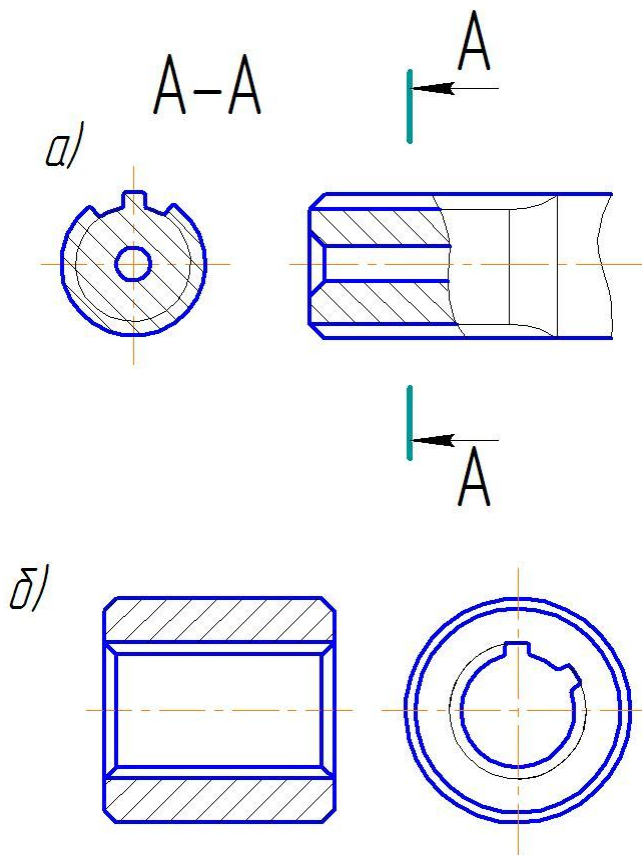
Изображение шлицевых вала и втулки с прямобочным профилем
